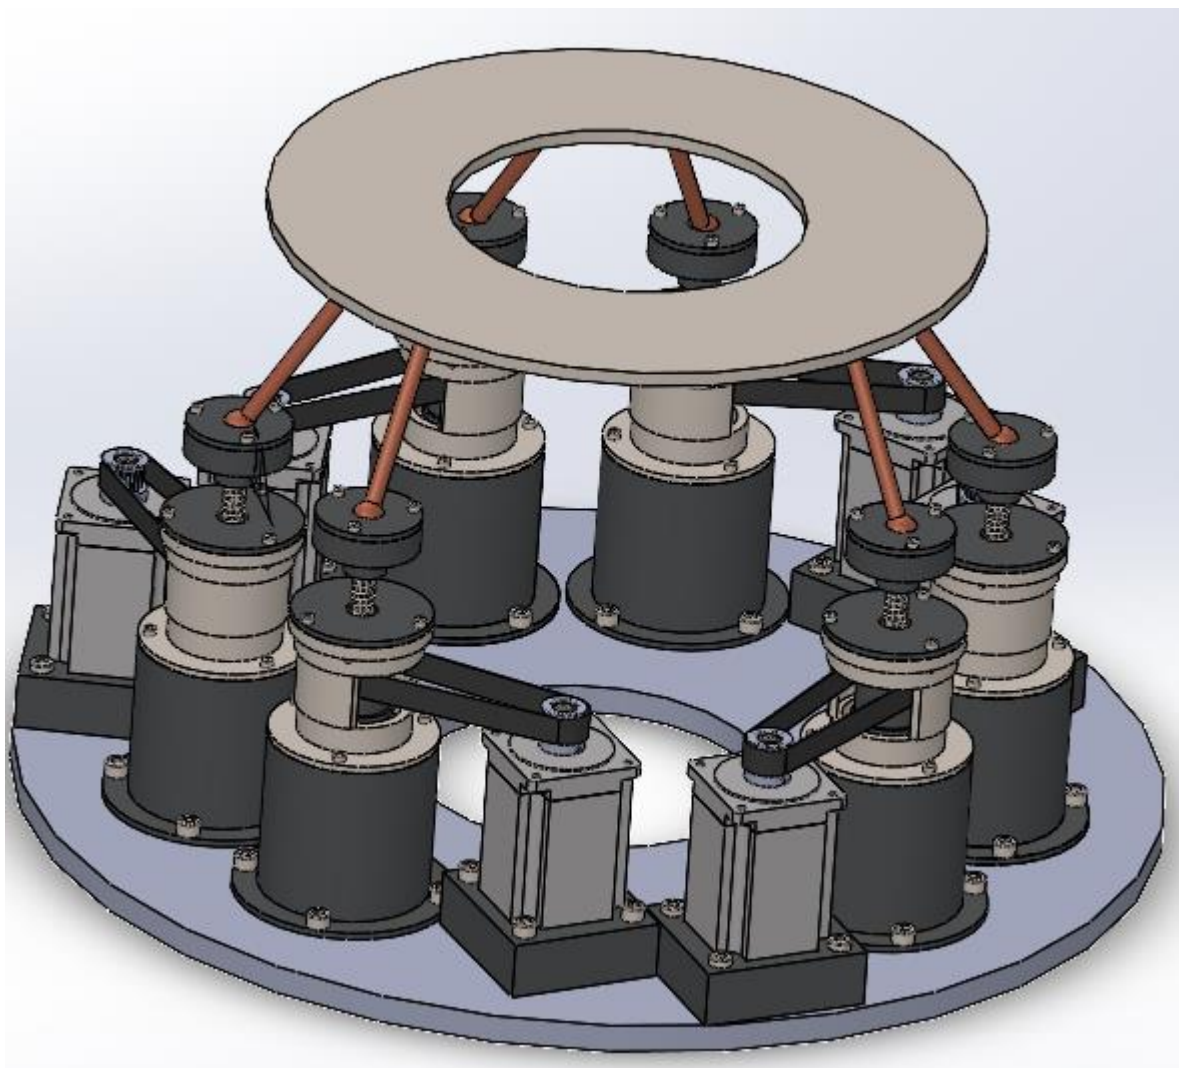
Габаритная компоновка шести степенного
